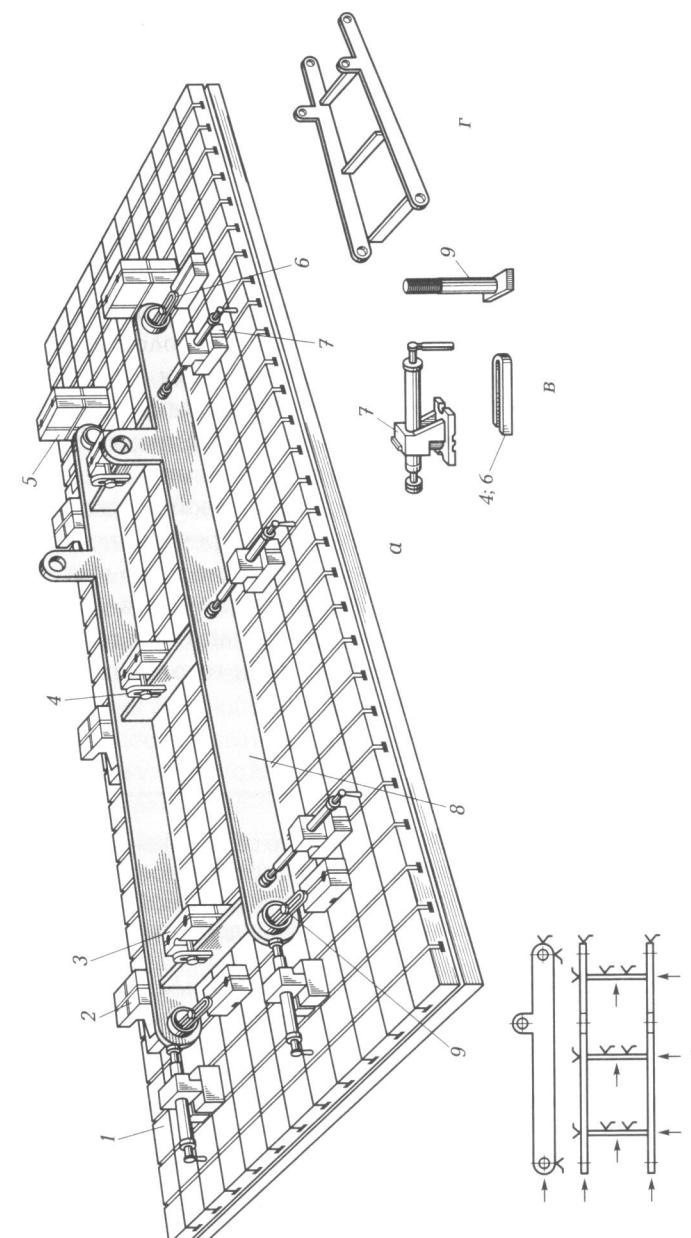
Компоновка УСП для сборки рамы [а], схема базирования [б], элементы УПС [в] и готовая рама [г]:
